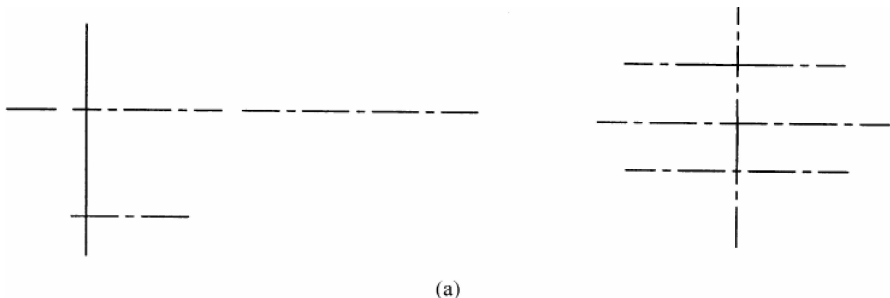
齿轮油泵装配图的绘制步骤-1
